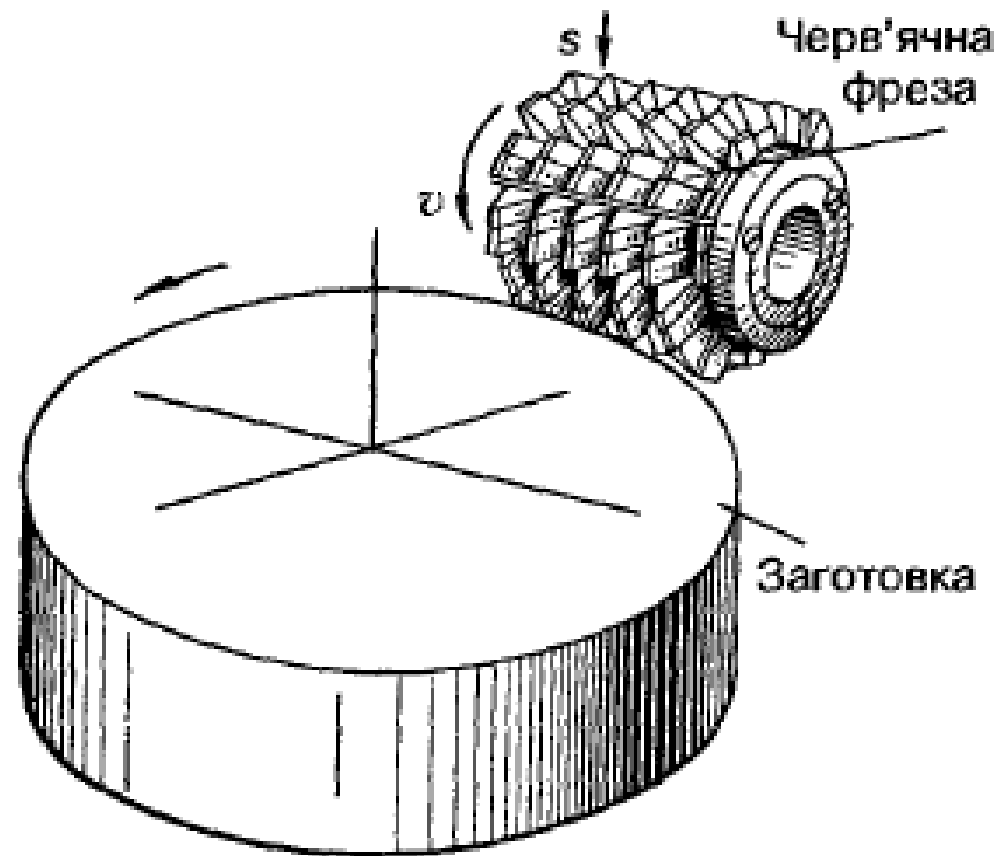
Фрезерування зубців зубчастих коліс черв'ячною модульною фрезою
